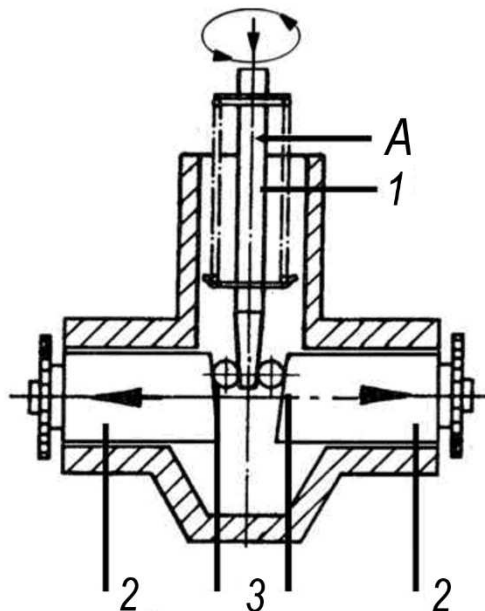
Регулировка автоматическая распорно-клинового механизма
